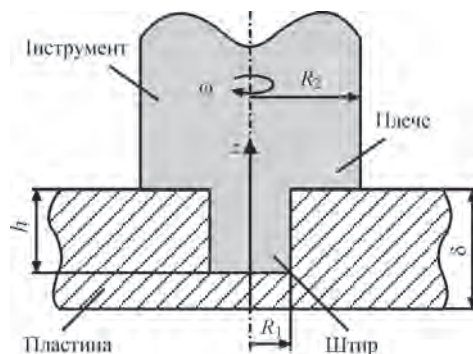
Схема робочого інструменту та пластин з'єднання при ЗТП
